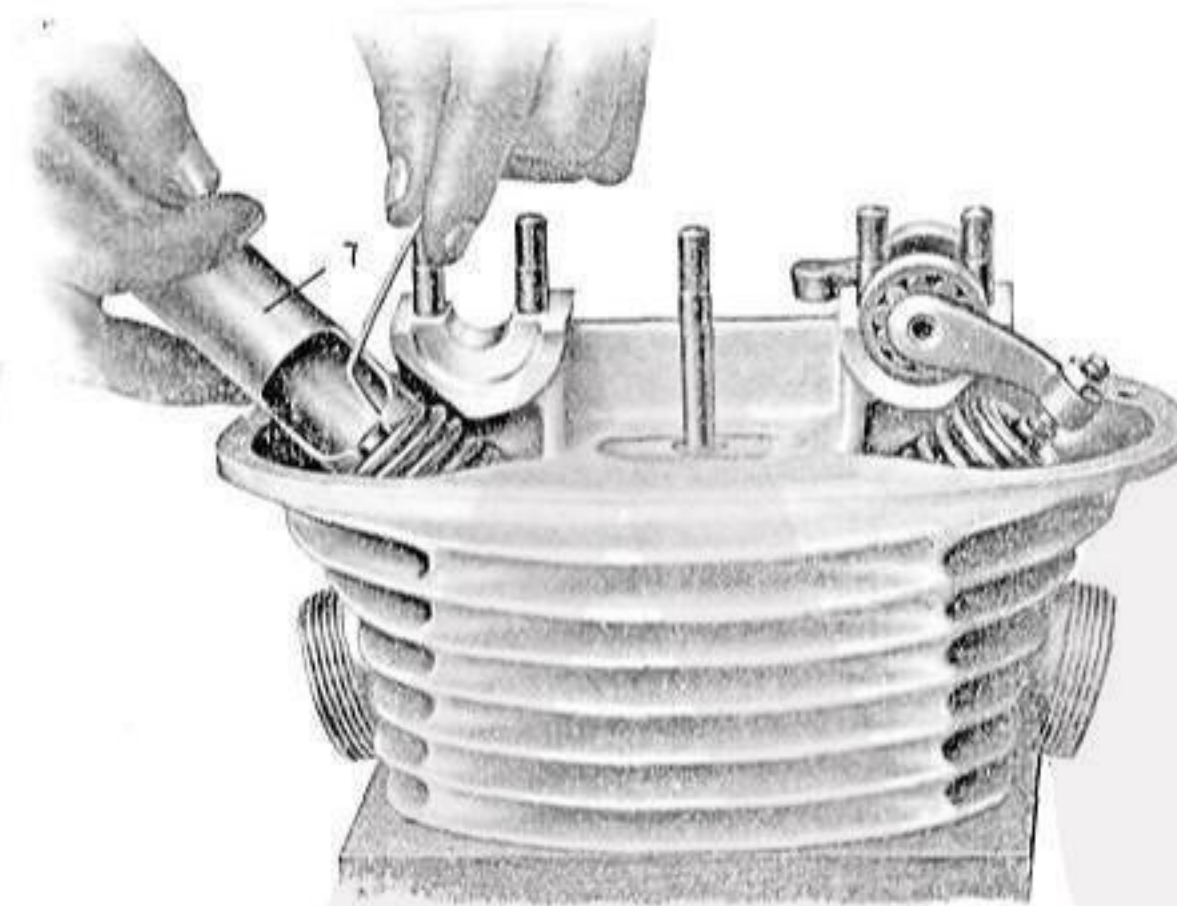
Ausbau der Ventile bei der Sportmaschine
